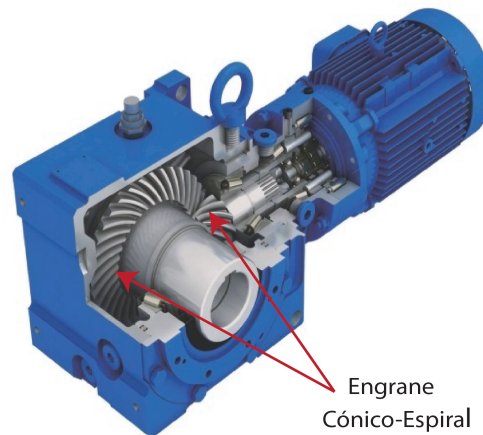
Reductores con Grupo Cónico-Espiral o de Velocidad de Engranaje
